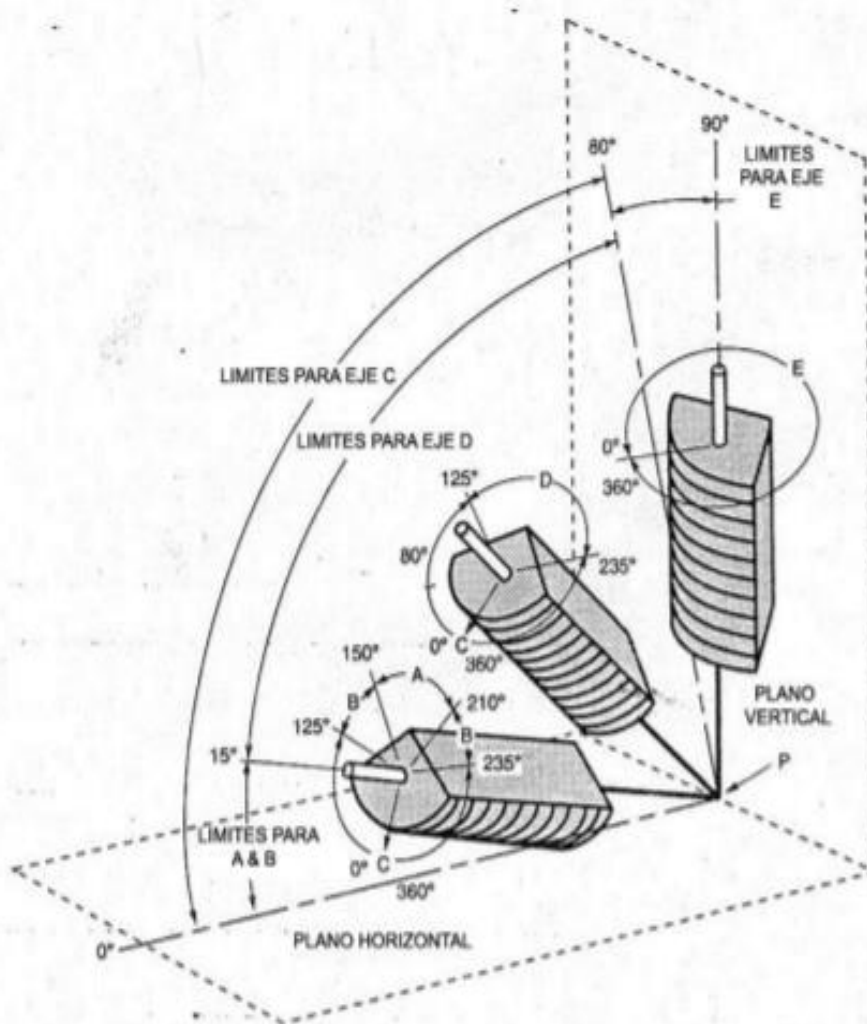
Posiciones de Soldaduras de Filete (ver 4.2.4)
